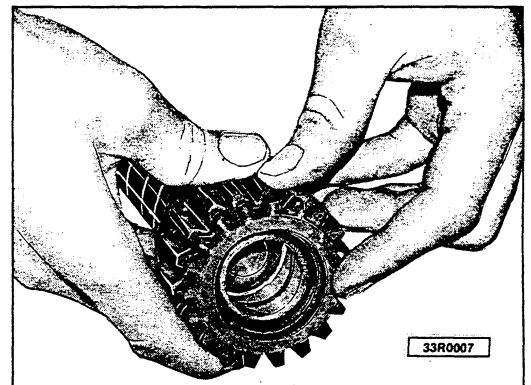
Control del desgaste de los dientes de los engranajes.
